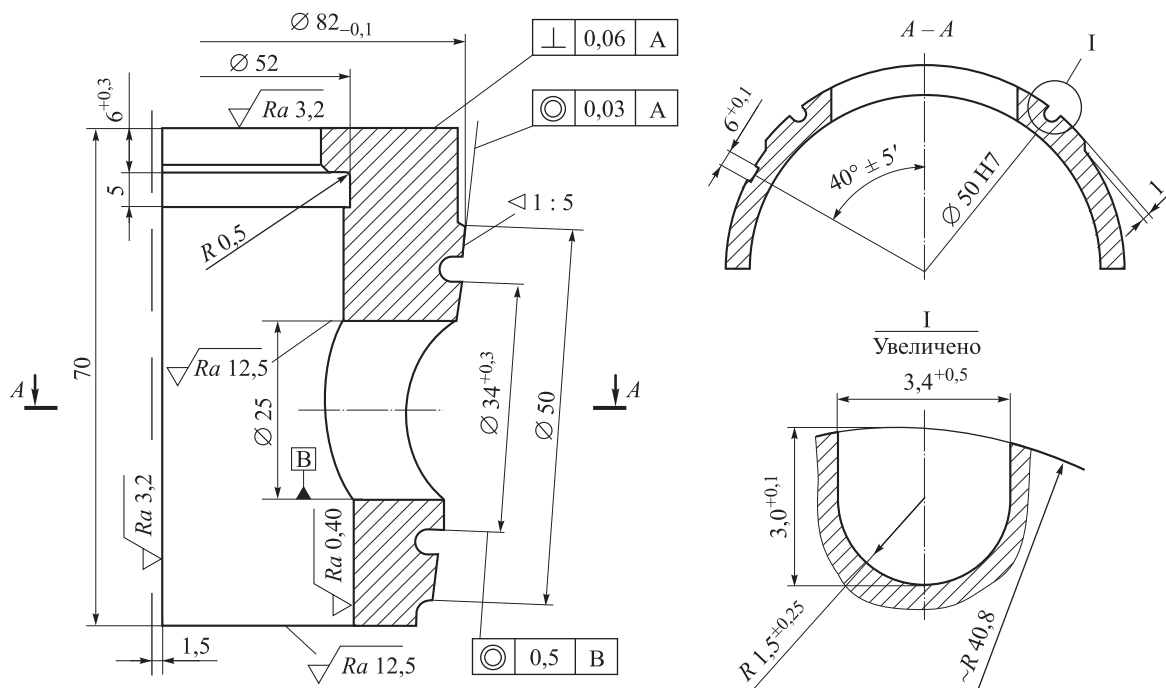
Эскиз конструкции детали «Вкладыш ЗРК 004»
